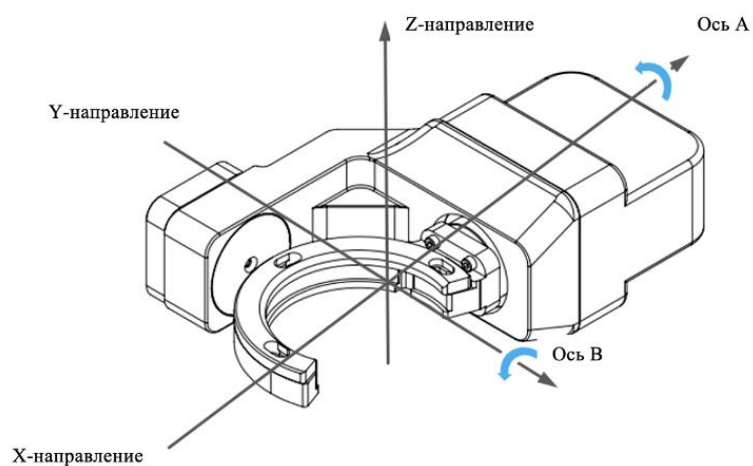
Оси фрезерования и вращения держателя для 5-осевых станков
